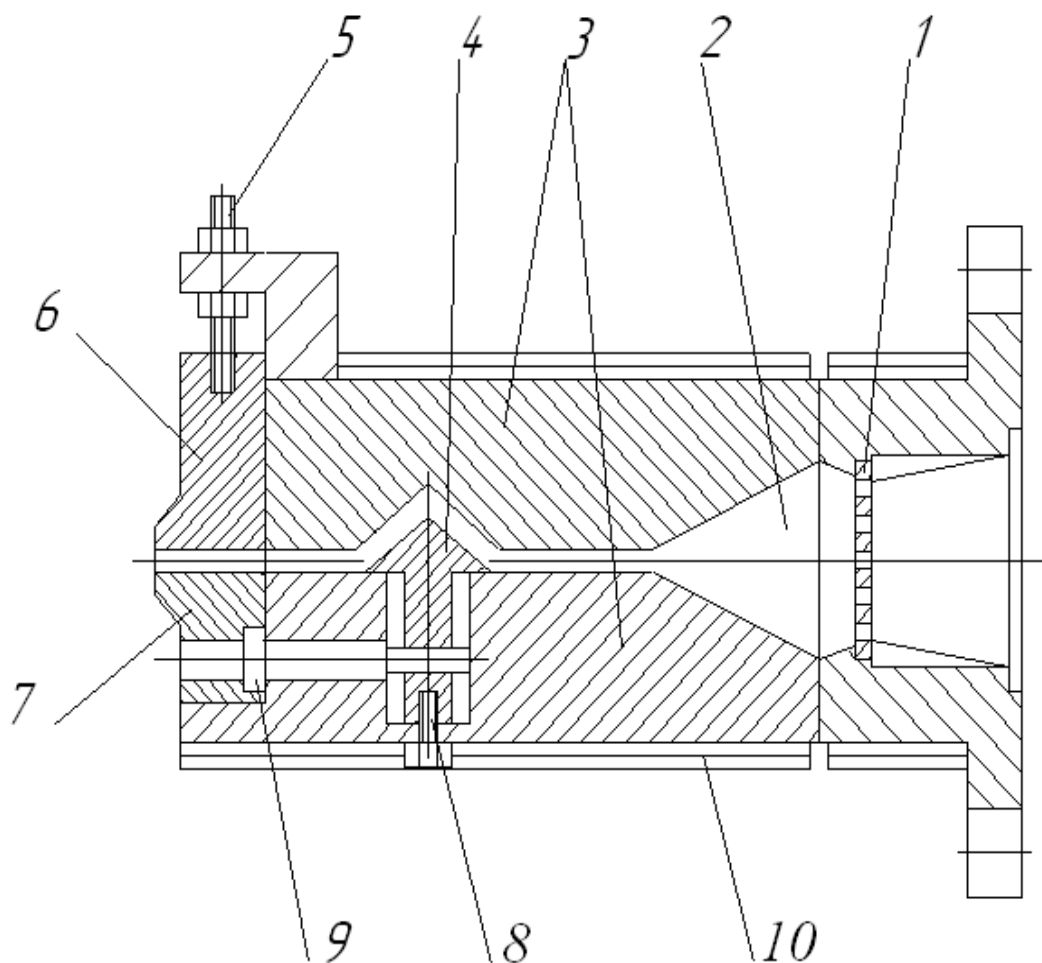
Конструкція щілинної головки з пристроєм для гідравлічного балансування:
